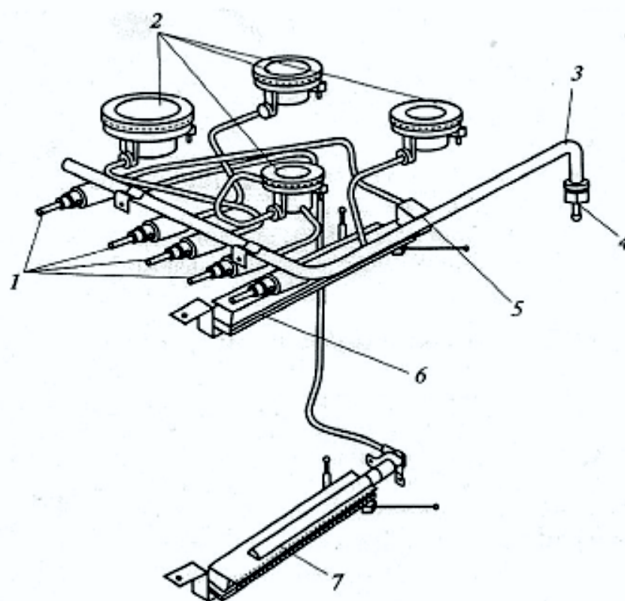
Конструкция газовой плиты: 1 — газовый клапан; 2 — газовые конфорки; 3 — главная труба подачи газа; 4 — переходник для подключения к подаче газа; 5 — труба подачи газа к конфоркам; 6 — гриль; 7 — горелка духовки
